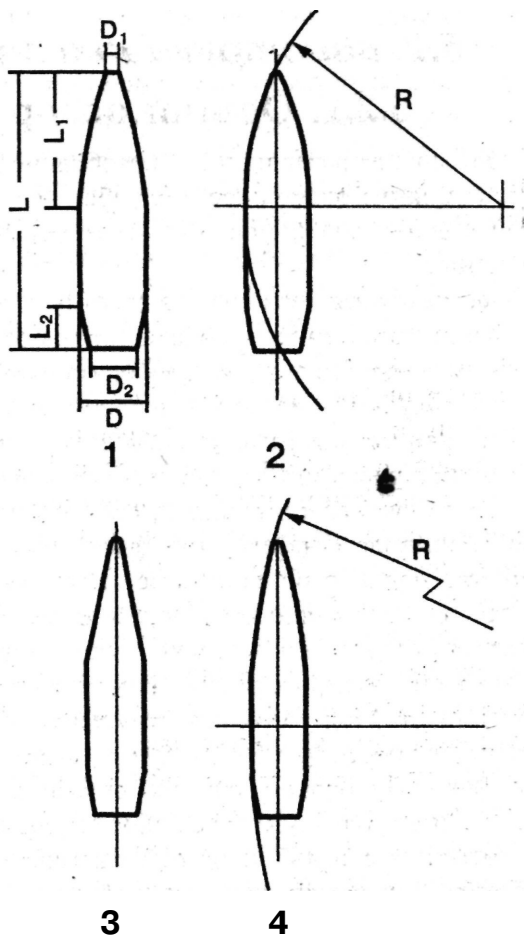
Размеры пули: 1 - общий вид; 2 - 4 - пули соответственно с тангенциальной, конической и секантной поверхностями носовой части; D - диаметр ведущей части; L - общая длина; D_1 - диаметр носика; L_2 - длина конусной хвостовой части (если пуля с цилиндрической донной частью $L_2=0$); D_2 - диаметр донца пули с конусной хвостовой частью (если пуля с цилиндрической донной частью $D_2=0$); R - радиус поверхности носовой части пули.
